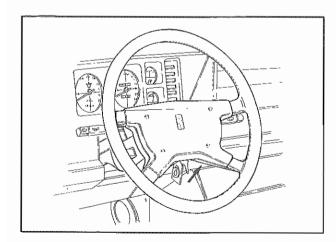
Viti di fissaggio ant. del volante Steering wheel front screws
